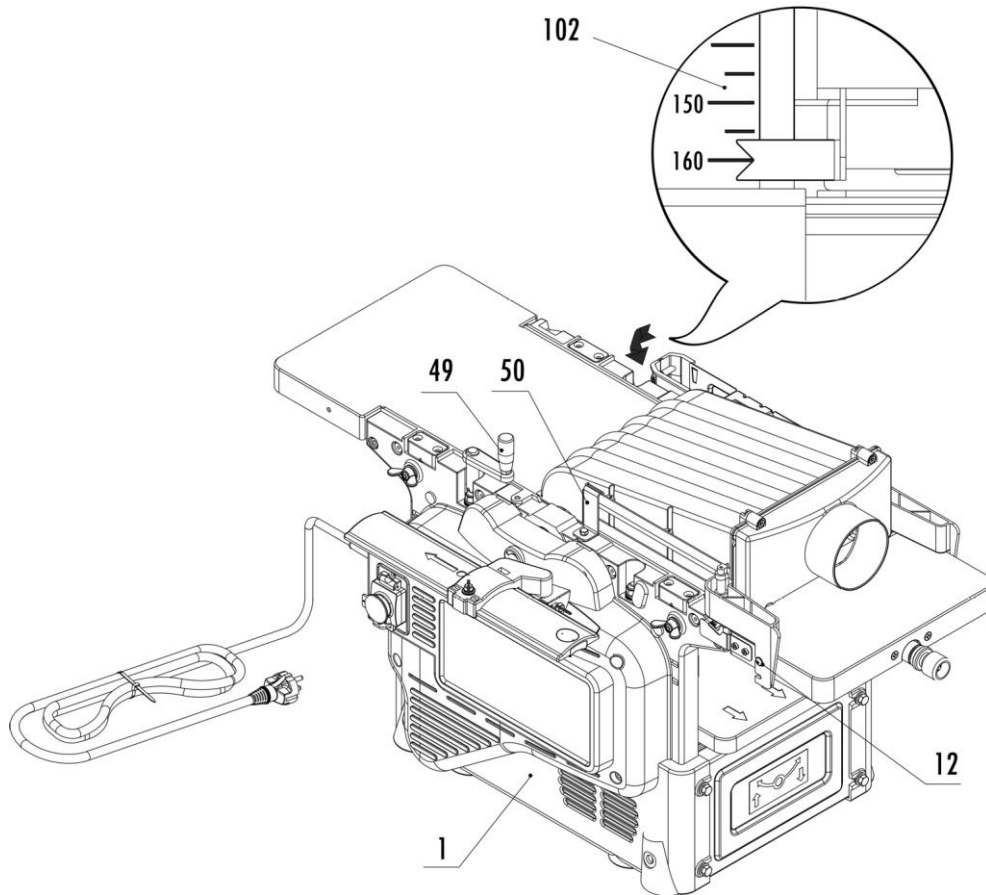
Станок деревообрабатывающий рейсмусовый.
